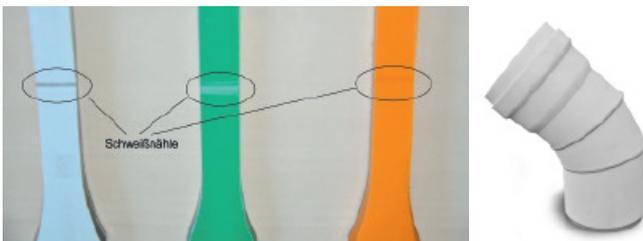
Geschweißte Probekörper und geschweißter Bogen
